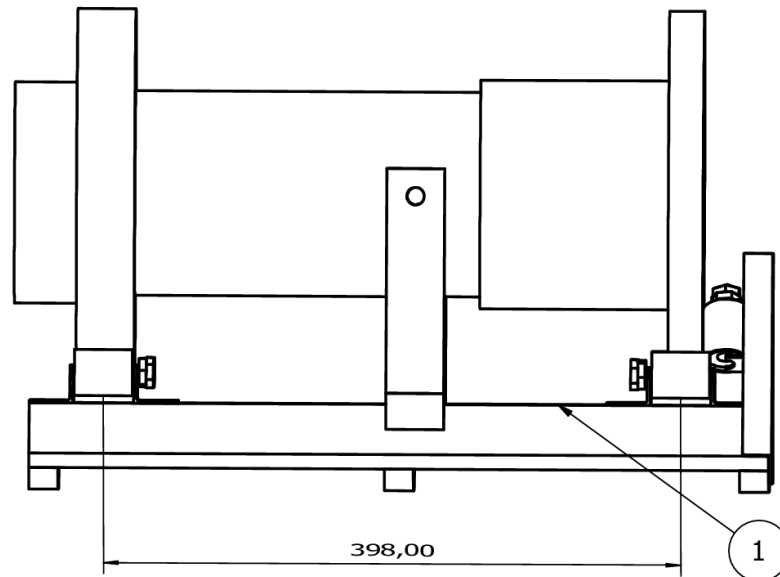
Diseño original de reactor montado en base de rodamientos.
